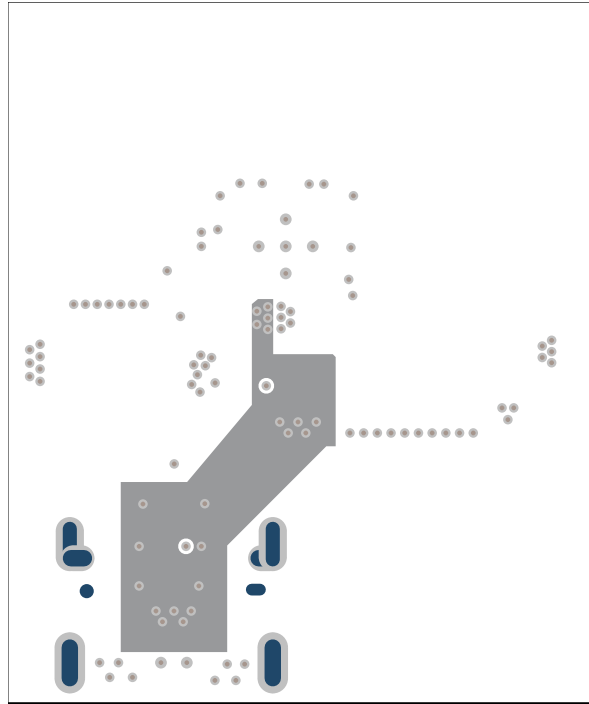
TPS25751S PCB Layout - Internal Power Layer
